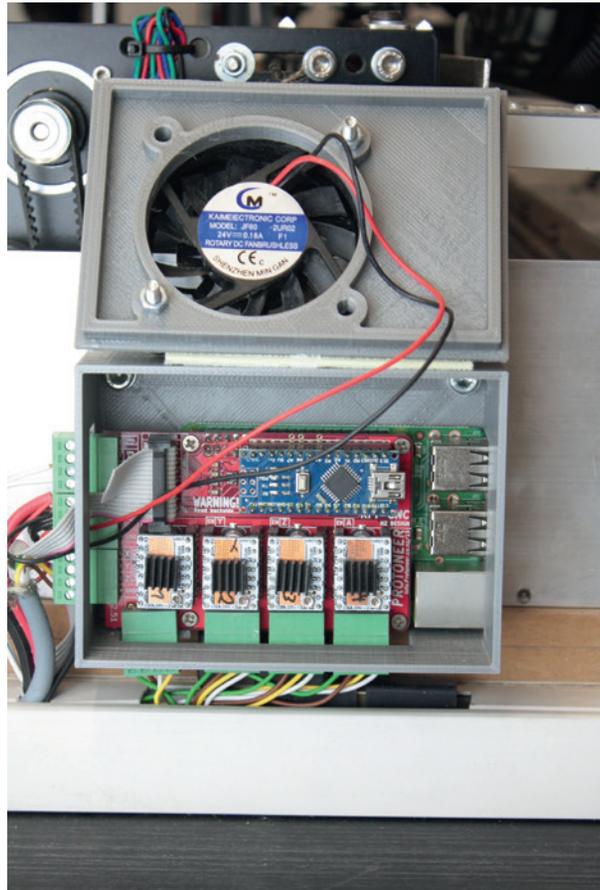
Dreamteam – die Arduino-Steuerung (hier auf einem älteren Protoneer-Board) mit Raspberry Pi als Steuerrechner: Das Gehäuse lenkt den Kühlstrom auf beide Platinen und stammt aus dem 3D-Drucker. Ein Kabelkanal am unteren Rand der Fräse verdeckt den Kabelsalat.
